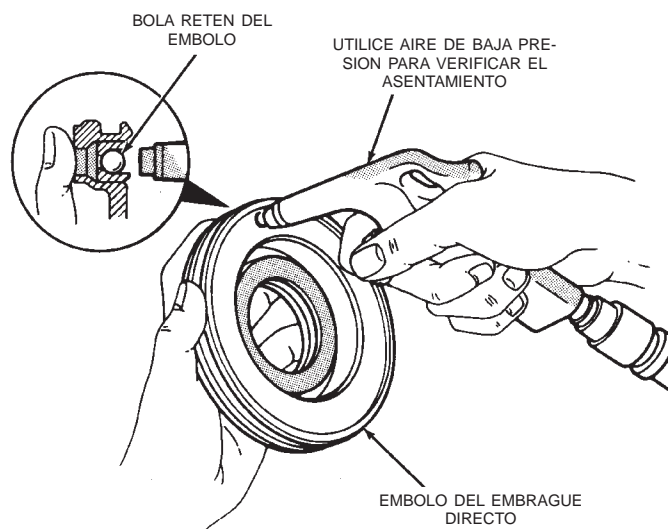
Prueba del asentamiento de la bola retén del émbolo
